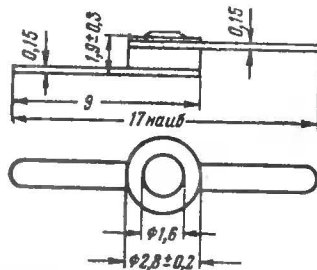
Габаритный чертеж диодов 3И302А—3И302Г.
